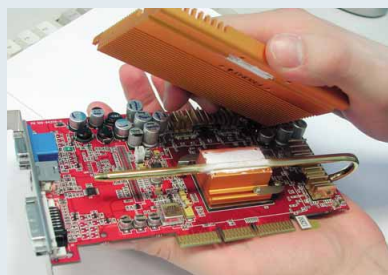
Setzen Sie die Kühlplatte auf den passenden Kühlblock. Verschrauben Sie beide anschließend.
